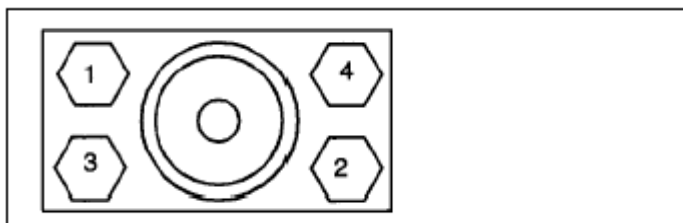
Obudowa modułu elektronicznego i łącznik mechaniczny
